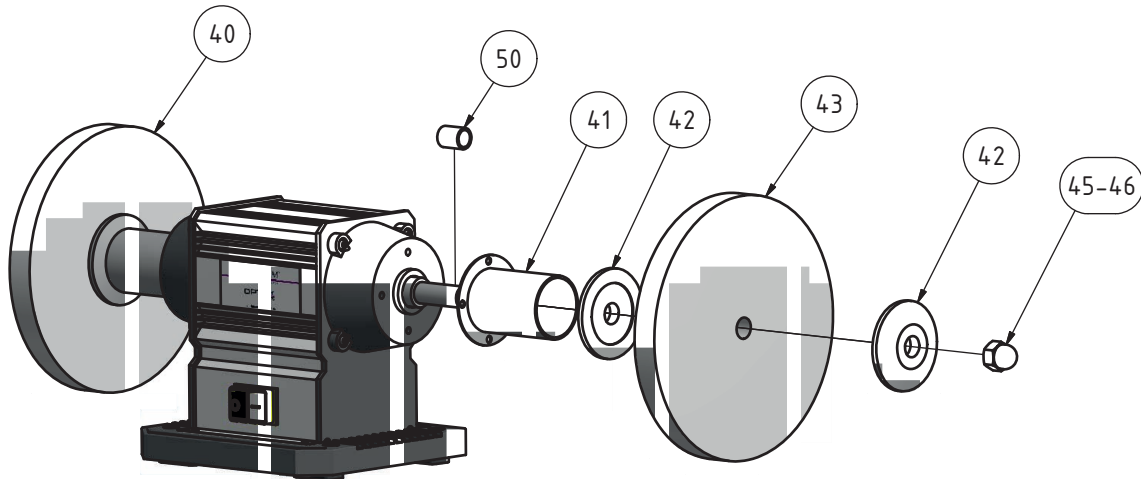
Ersatzteilzeichnung - Spare parts drawing
